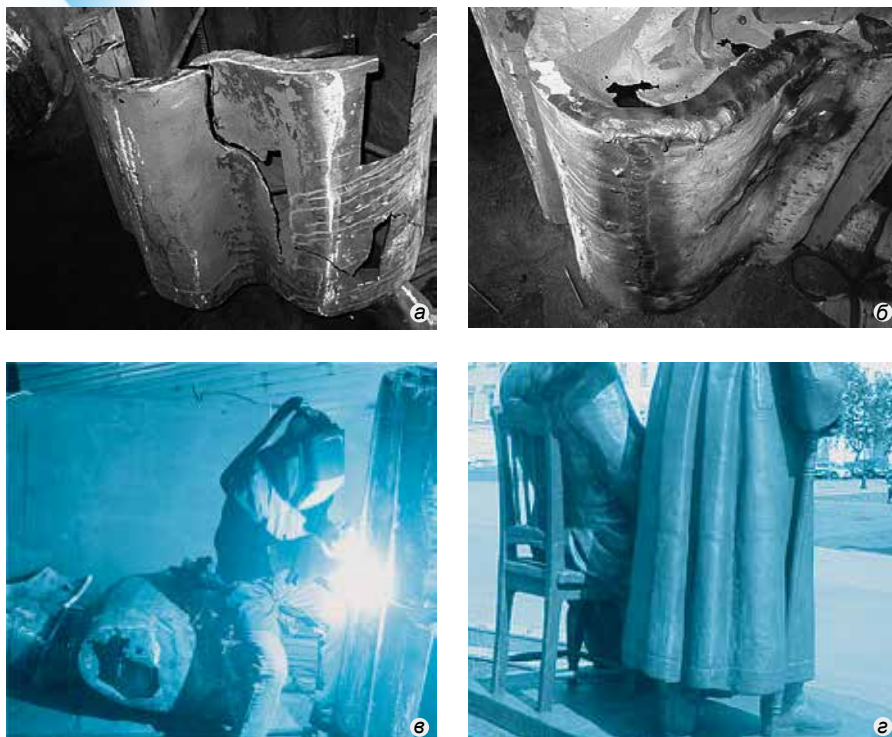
Плазменная сварка бронзового литья при изготовлении монумента; а, б – исходное состояние заготовки (нижняя часть стоящей фигуры); в – сварка блоков фигуры; г – состояние после сварки.
